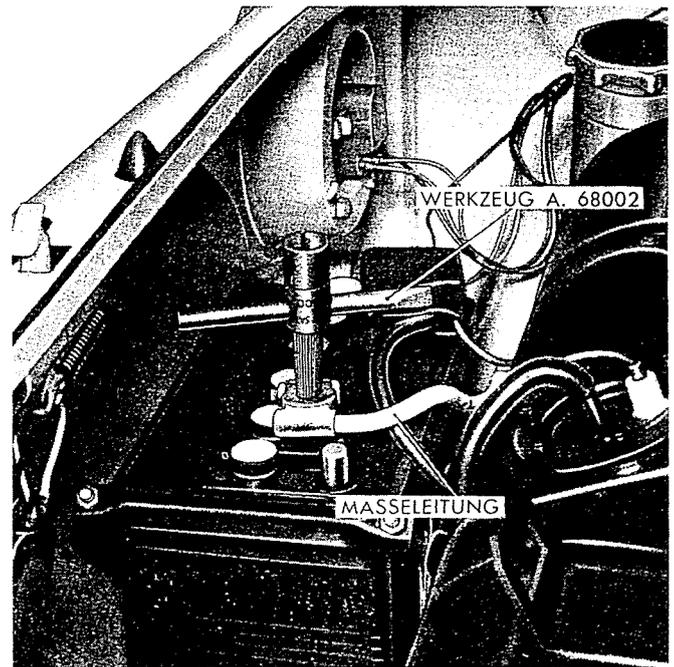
Reinigung der Batterieklemmen mit dem Werkzeug A. 68002.
